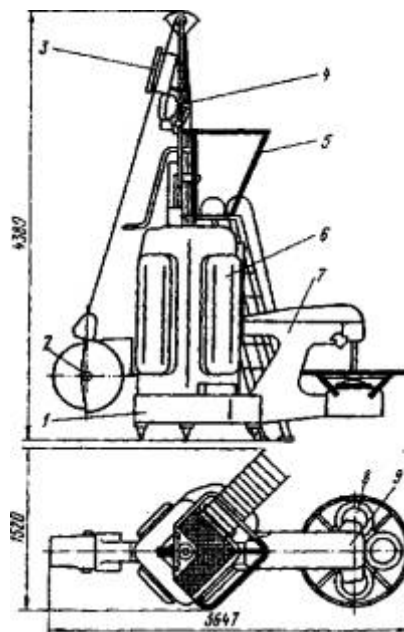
Фасувально-пакувальний автомат Д9-АП1НМ для фасування молока в тетраедричні пакети: 1 – литий корпус; 2 – розмотувальний пристрій з датувальним механізмом; 3 – ультрафіолетова лампа; 4 – формувальний пристрій; 5 – робоча платформа; 6 – протяжний механізм; 7 – ковшовий елеватор; 8 – пристрій укладання; 9 – зона укладання
